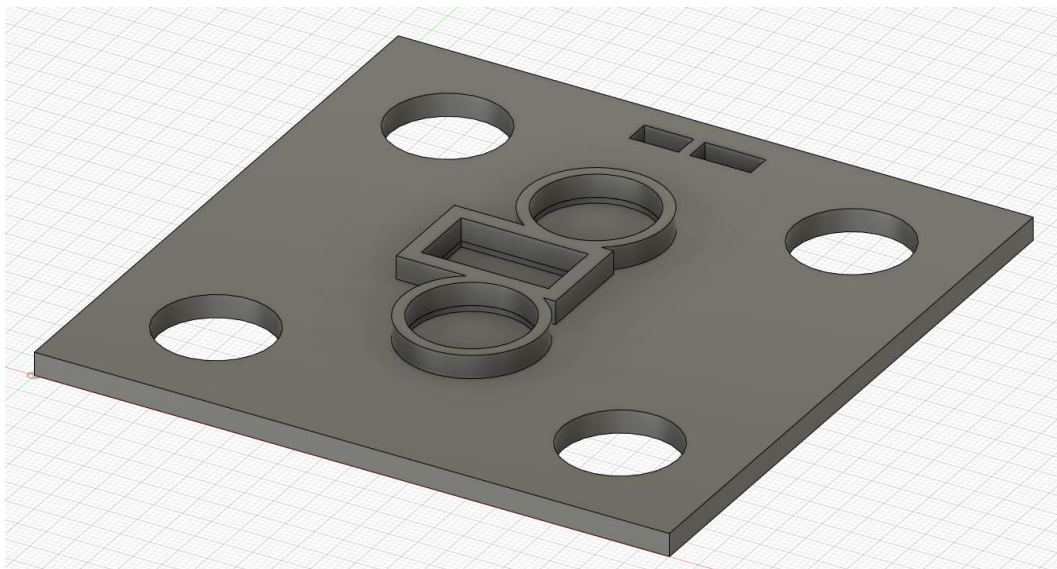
Нижня поверхня корпусу з додатковим корпусом для кріплення сервоприводу та електромагніту
